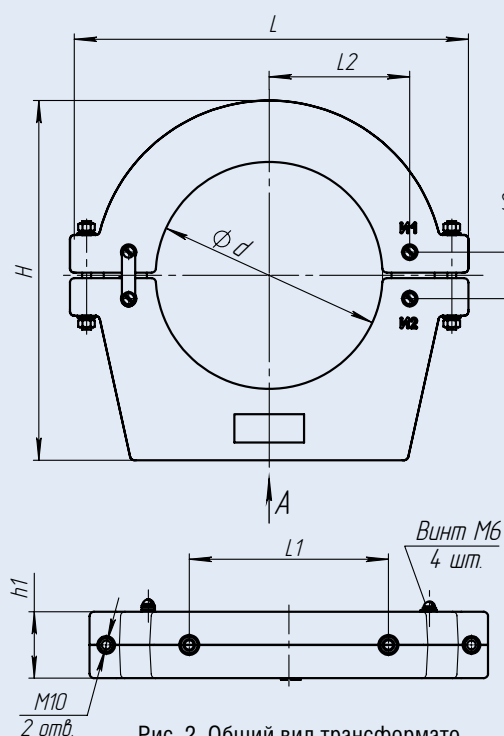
Общий вид трансформатора тока ТЗРЛ для защиты
